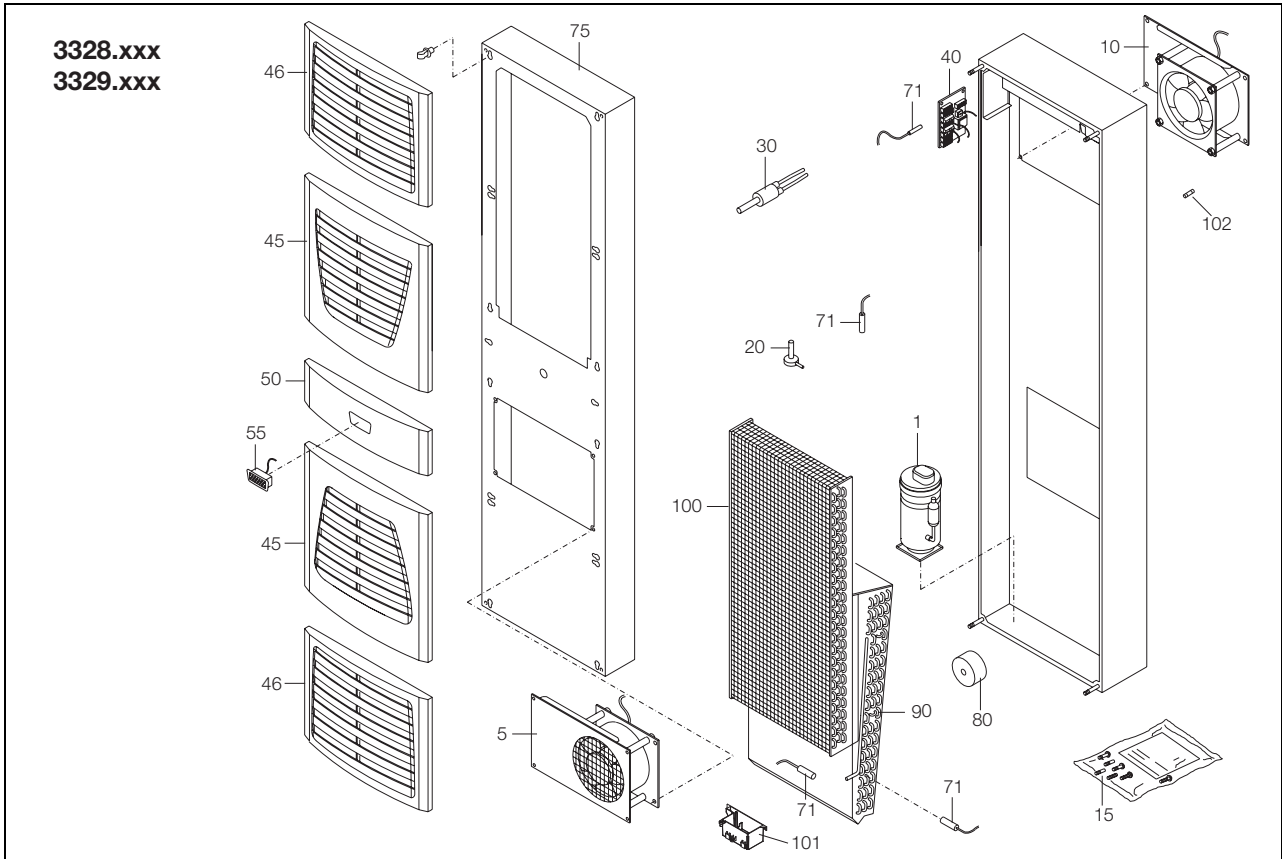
Pièces de rechange 3328.xxx, 3329.xxx
